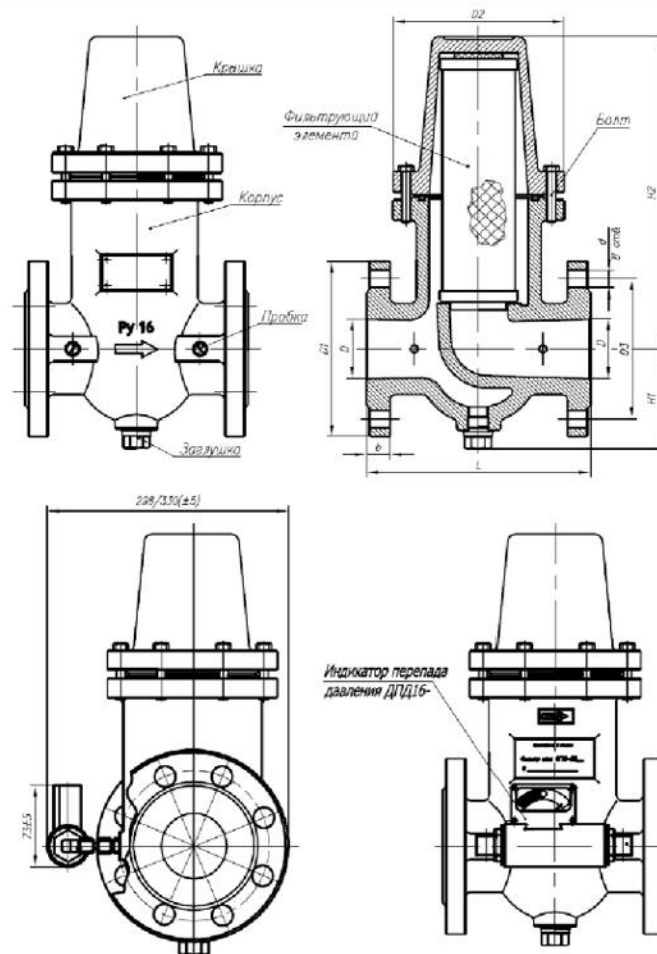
Габаритно-присоединительные размеры фильтров: ФГ16-80, ФГ16-80-В, ФГ16-100, ФГ16-100-В
